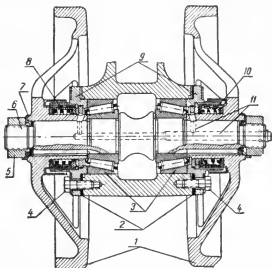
Регулировка подшипников опорных катков тракторов ДТ-54, ДТ-54А и Т-75:
